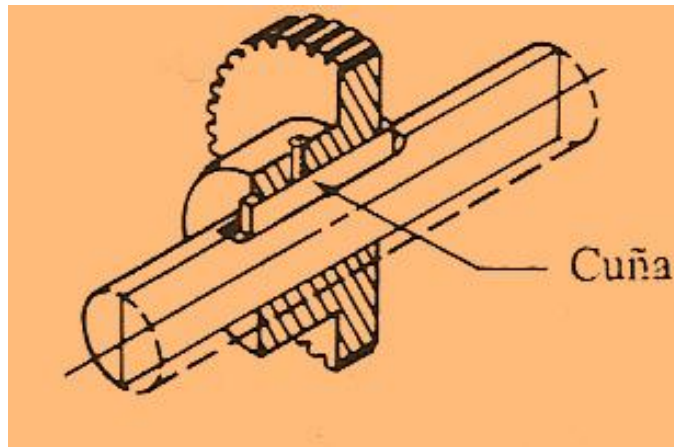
Ensamble flecha-engrane utilizando una cuña.
